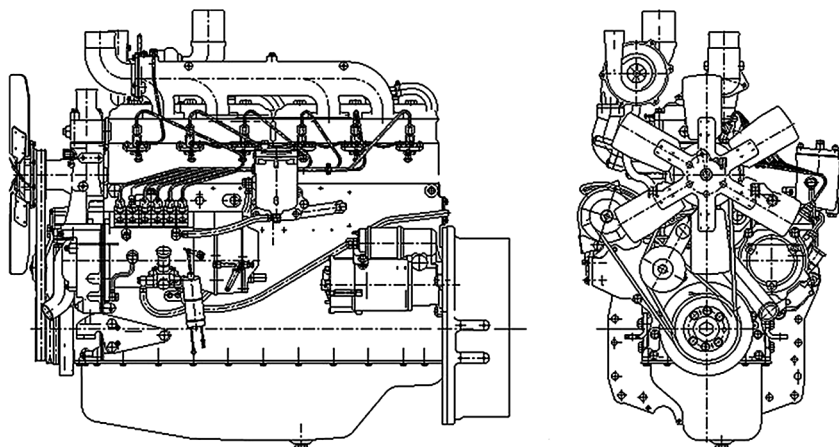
Двигатель внутреннего сгорания – сборочная единица 1-го порядка грузового автомобиля
